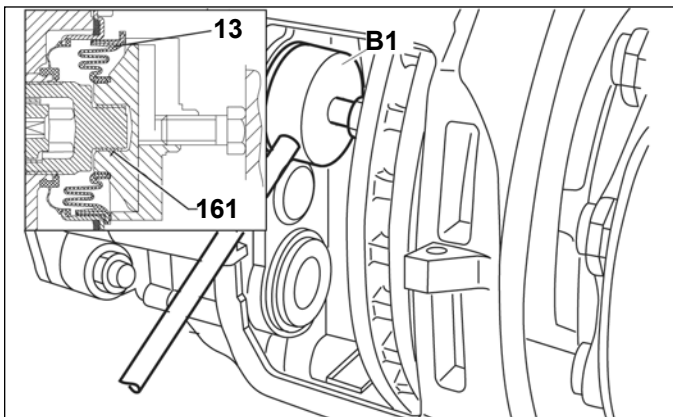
INSTALLATION DU POUSSOIR ET DU CACHE-POUSSIÈRE SUR LE VÉHICULE
